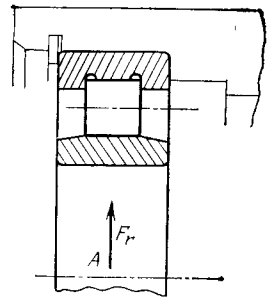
Схема подшипника с цилиндрическими роликами.
